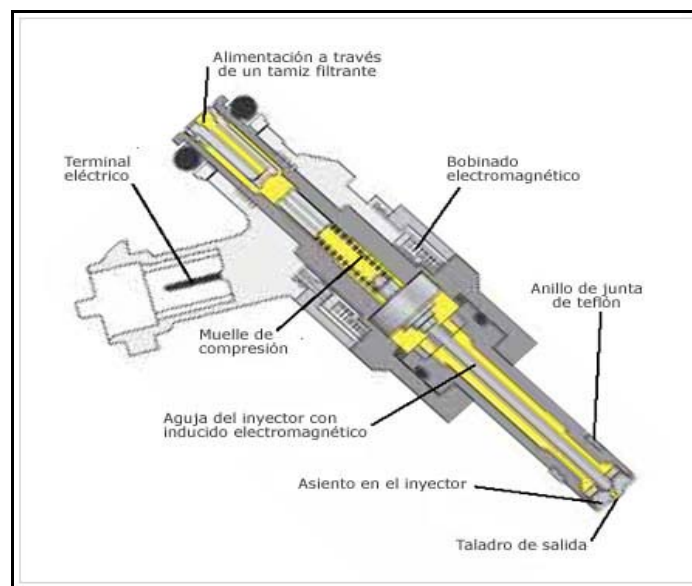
Corte de un inyector de combustible.⁵⁹
